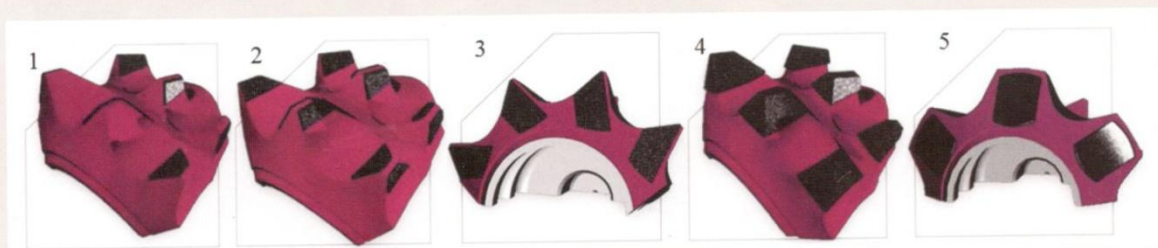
Схемы армирования фрезерованных зубьев: 1 – наплавляется только одна грань; 2 – наплавляется набегающая грань и часть сбегающей грани; 3 – наплавляются полностью торцы Г- и Т-образных зубьев; 4 – Т-усиленная объемная наплавка зубьев; 5 – W-усиленный периферийный (калибрующий) ряд.
